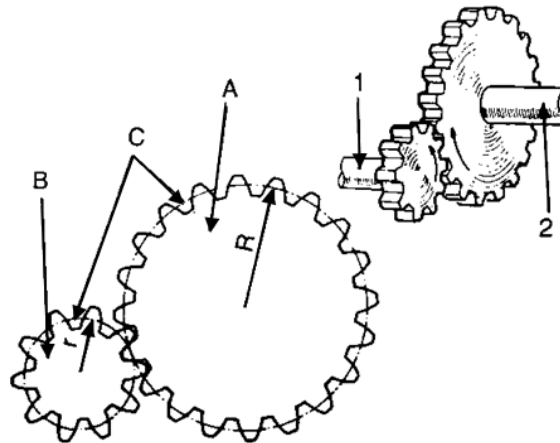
Conjunto de engranaje. (de Castro, 1998)
